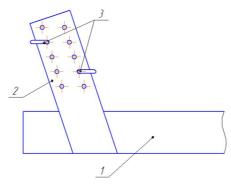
Регулировка высоты прикатывающего катка 1.Рама 2. Пластина регулировочная. 3.Палец стопорный
